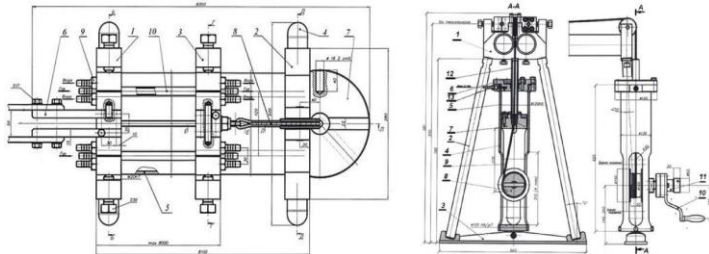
Общий вид (вид сверху) установки электроконтактного нагрева труб: 1 – передняя поперечина; 2 – задняя поперечина; 3 – подвижная поперечина; 4 – опора; 5 – станина; 6 – шина токоподвода; 7 – пневматическое устройство натяжения; 8 – канат; 9 – штуцер системы охлаждения; 10 – нагреваемая труба
